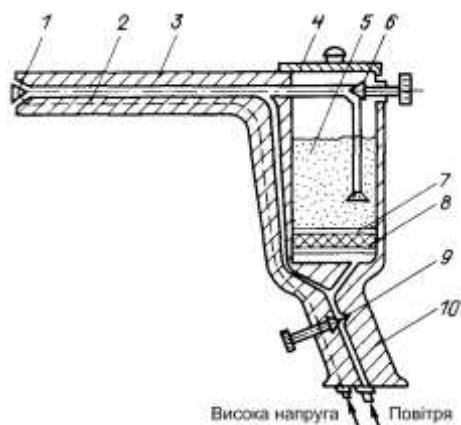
Схема пневматичного розпилювача порошкового матеріалу.
